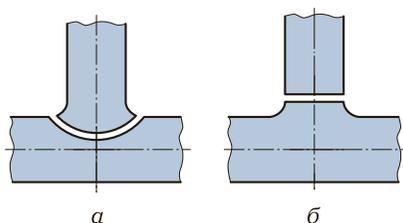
Схемы подготовки под сварку трубчатых соединений из меди:
